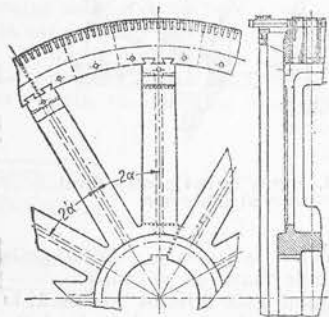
Fixarea tolelor sector ale rotorului prin coadă de rândunică.
